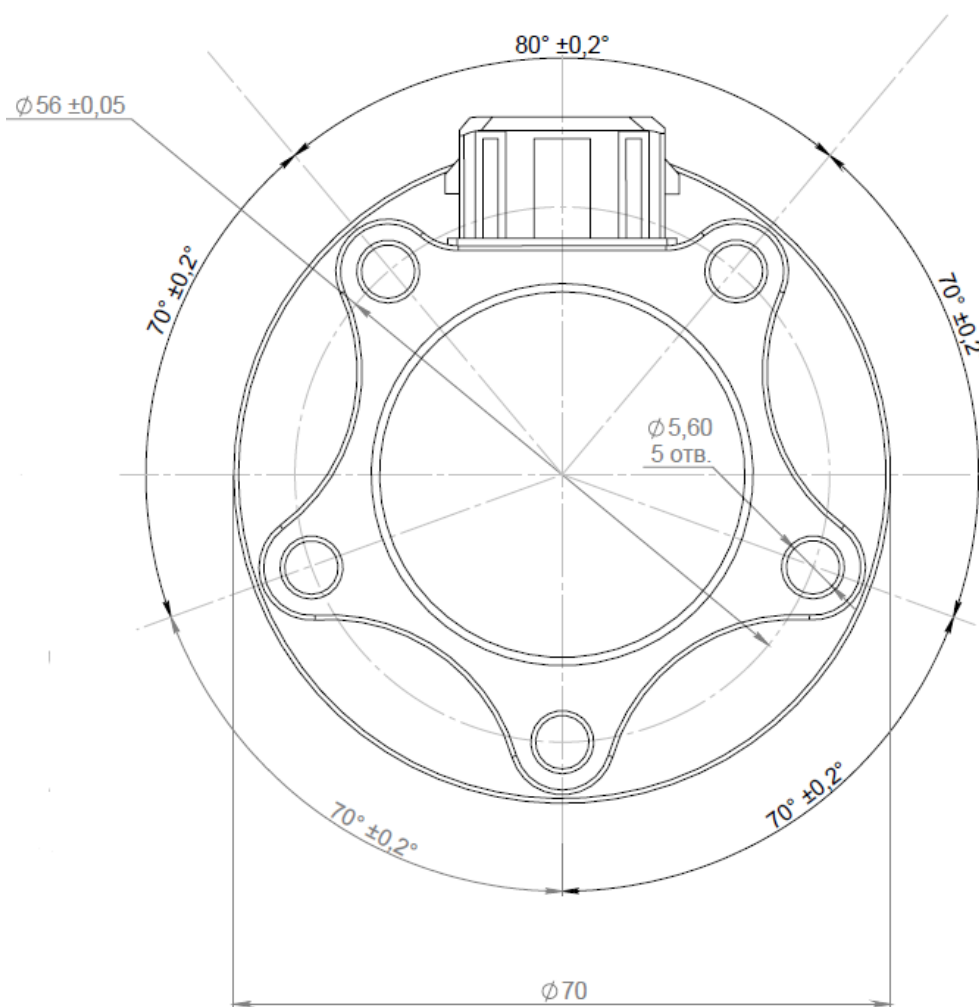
Схема расположения отверстий под крепёжные элементы
